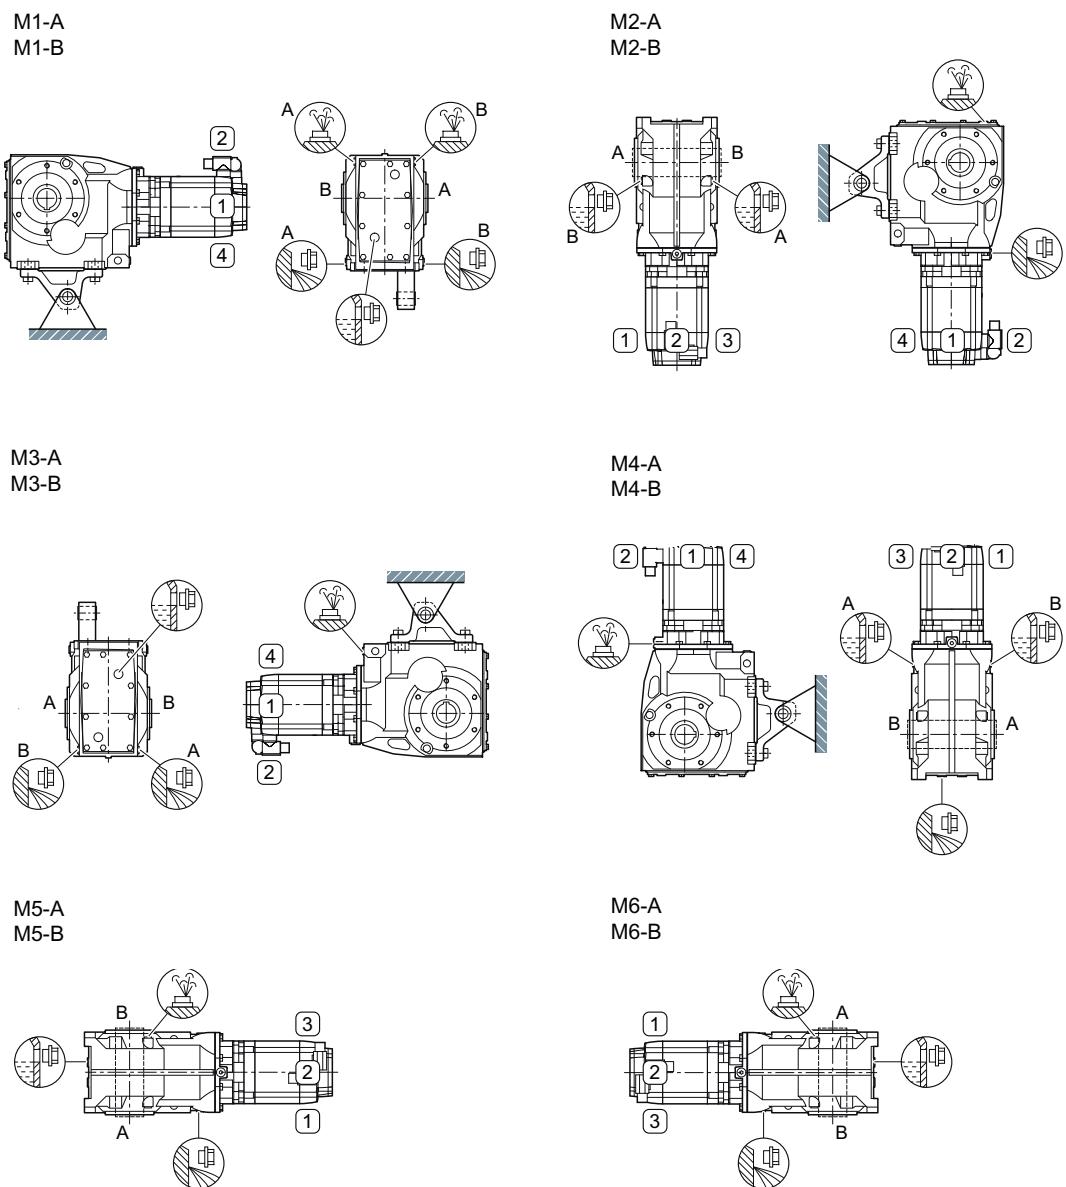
Einbaulagen für Servo-Kegelradgetriebemotor KAD, Aufsteckausführung, Baugrößen 39 - 149, 3-stufig
